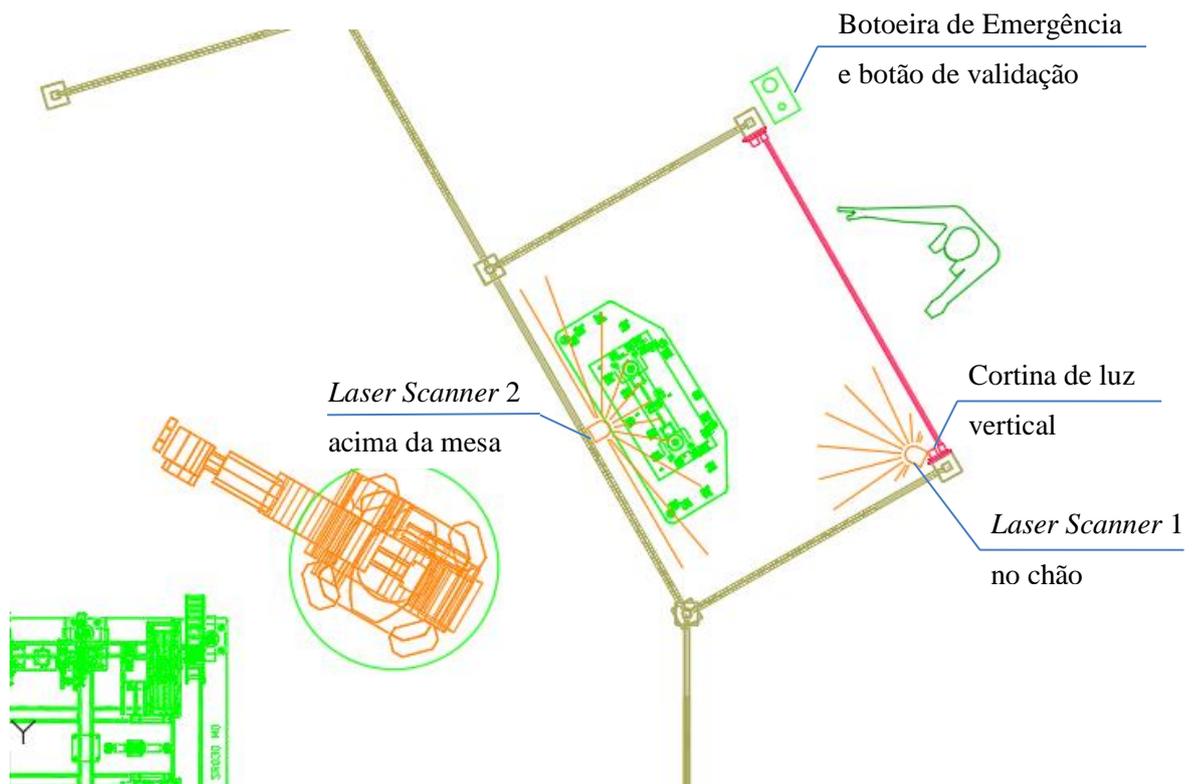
Layout* proposto para instalação dos dispositivos de proteção
